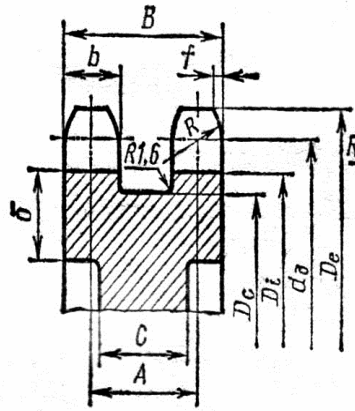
Конструювання зірочки ланцюгової передачі
